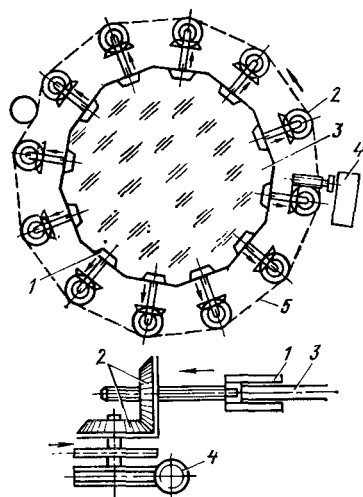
Схема получения ориентированных листов органического стекла круглой формы: 1 — захваты; 2 — тянущий узел; 3 — органическое стекло; 4 — редуктор; 5 — цепь
